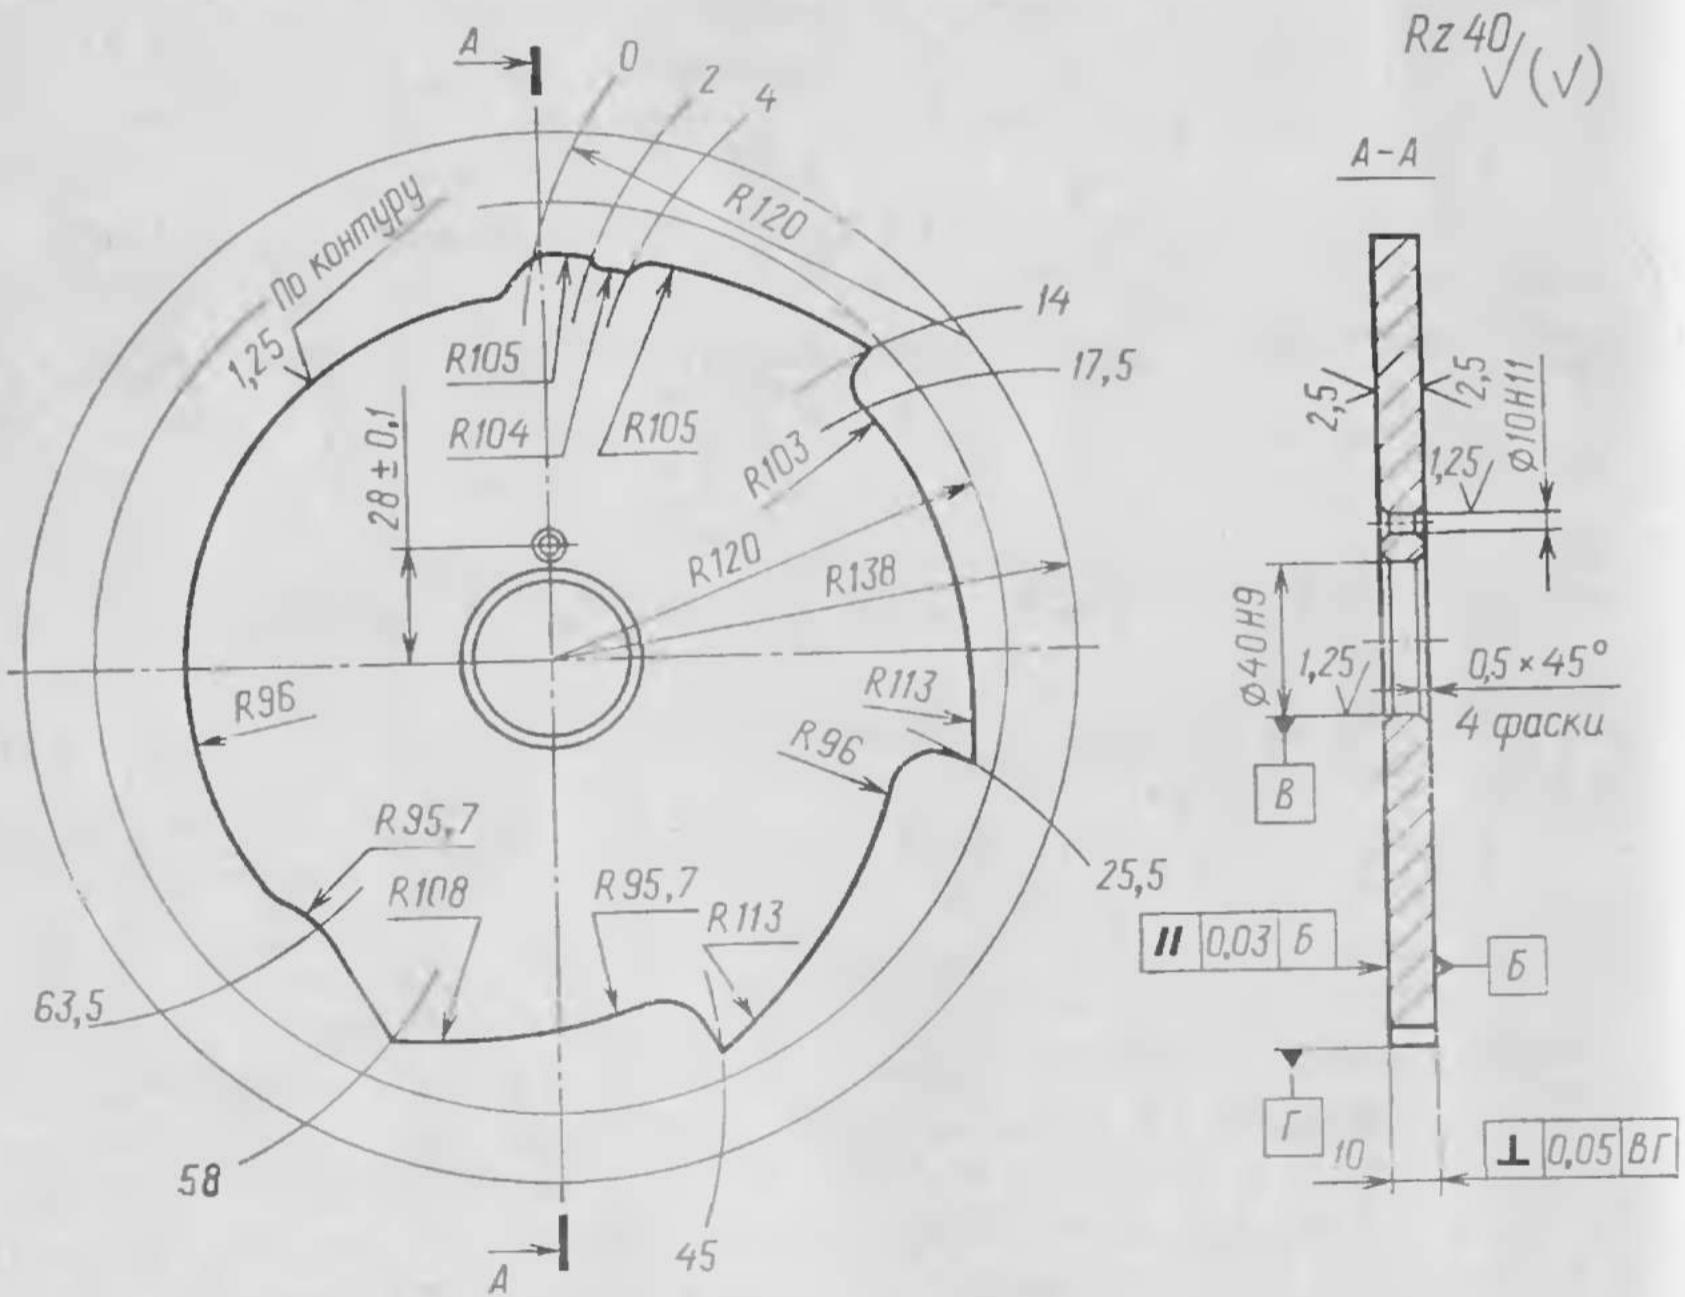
Чертеж кулачка револьверного суппорта для рассмотренного примера
